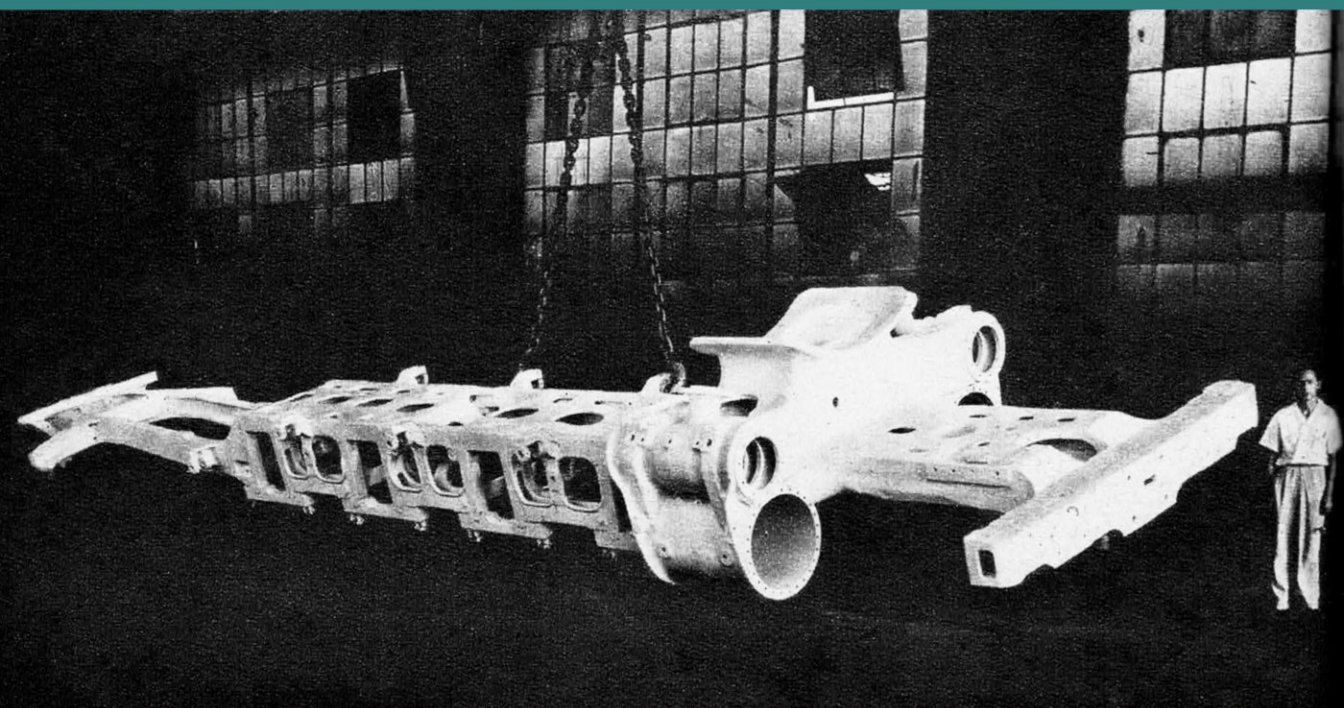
CHASSIS EN ACIER COULÉ D'UNE SEULE PIÈCE QUI ÉQUIPERA 200 LOCOMOTIVES 141-R
